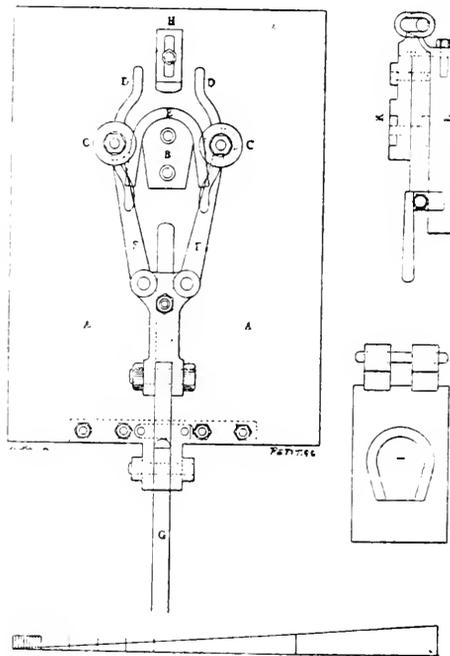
MACHINE A CENTRER (Fuzelier).
